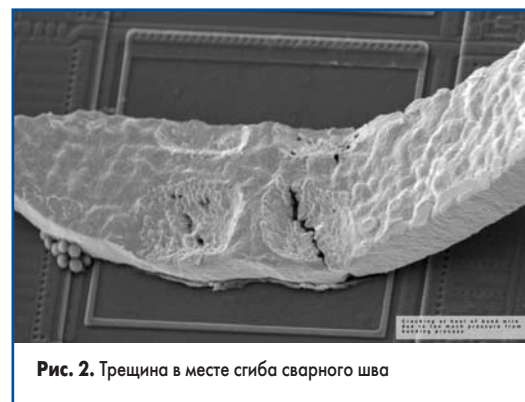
Трещина в месте сгиба сварного шва
